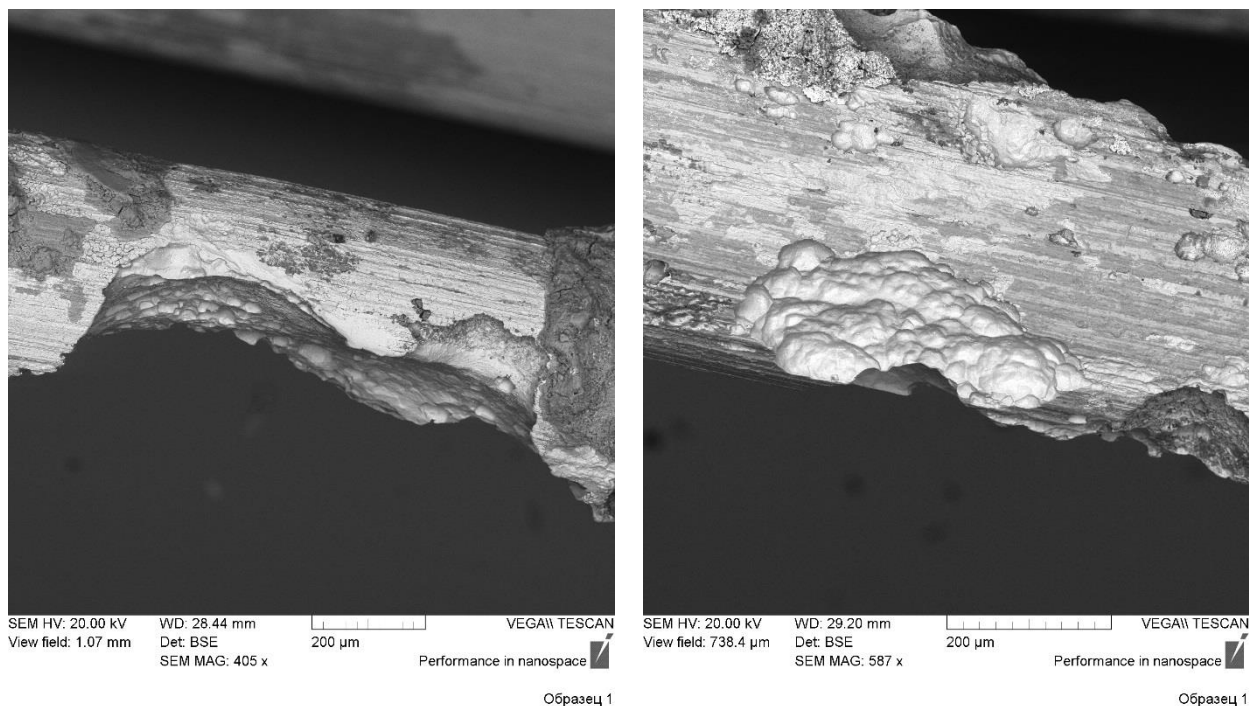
Крупный план повреждений нагревательной спирали тепловентилятора, СЭМ
